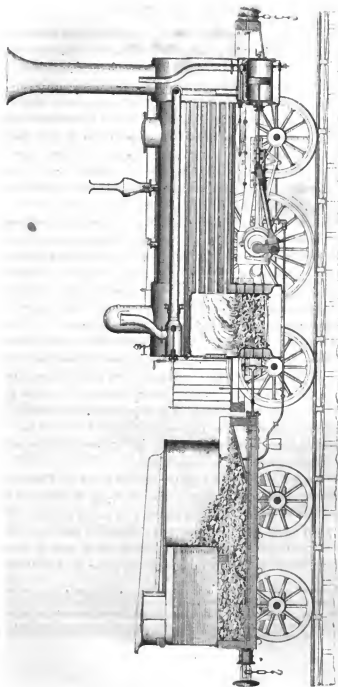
Coupe d'une machine locomotive et de son tender.
